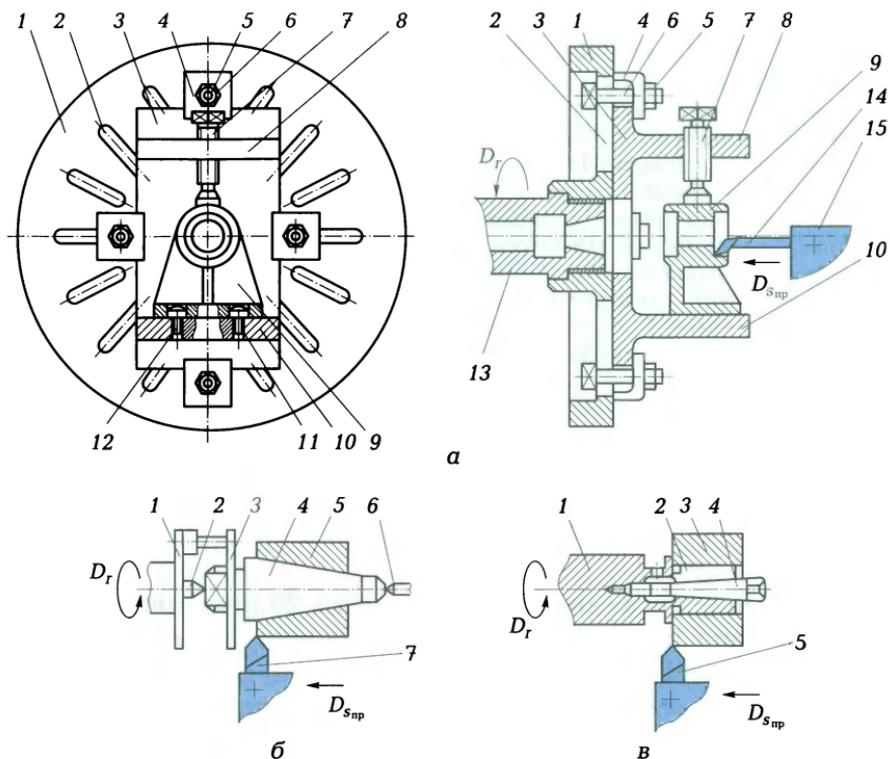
Схемы обработки заготовок на планшайбе и на оправках на токарно-винторезных станках:
